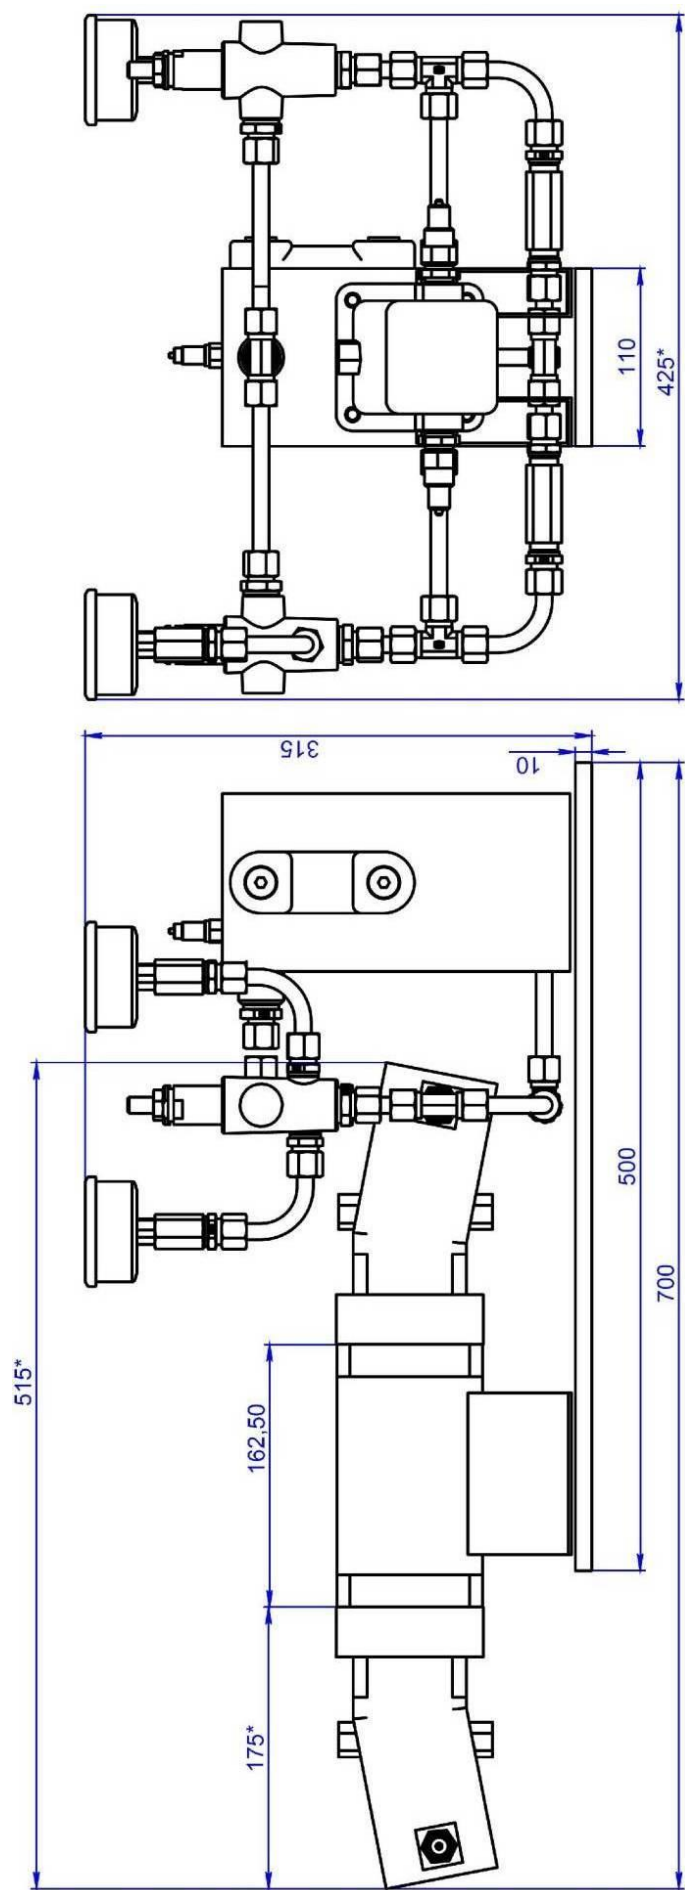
Габаритный чертёж нагружателя вращательного действия
